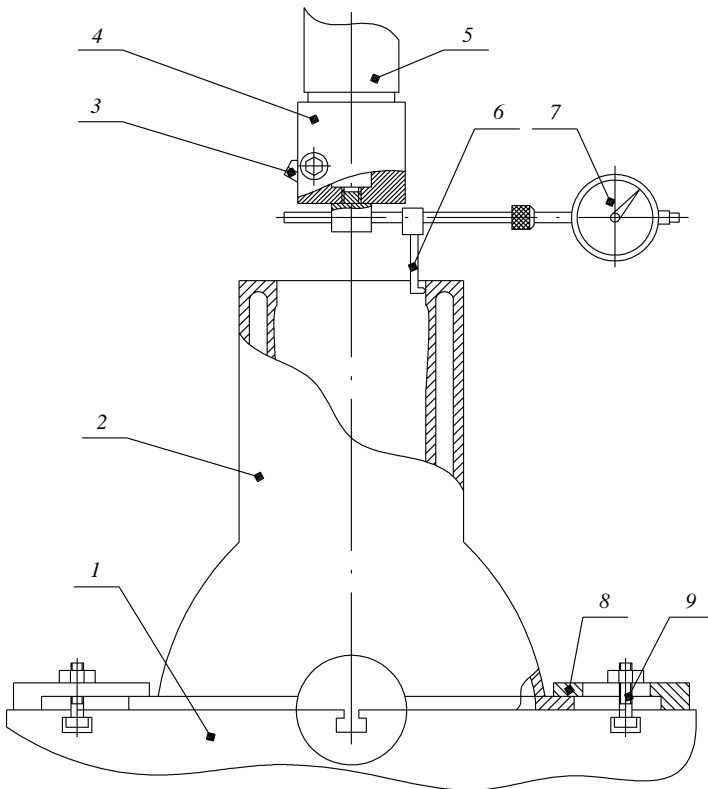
Приспособление для центровки цилиндра блока: 1 – стол станка; 2 – блок цилиндров двигателя; 3 – резец; 4 – резцовая головка; 5 – шпindelь; 6 – ножка индикаторного приспособления совмещения оси цилиндра с осью шпинделя; 7 – индикатор приспособления; 8 – прихват; 9 – крепежный болт
